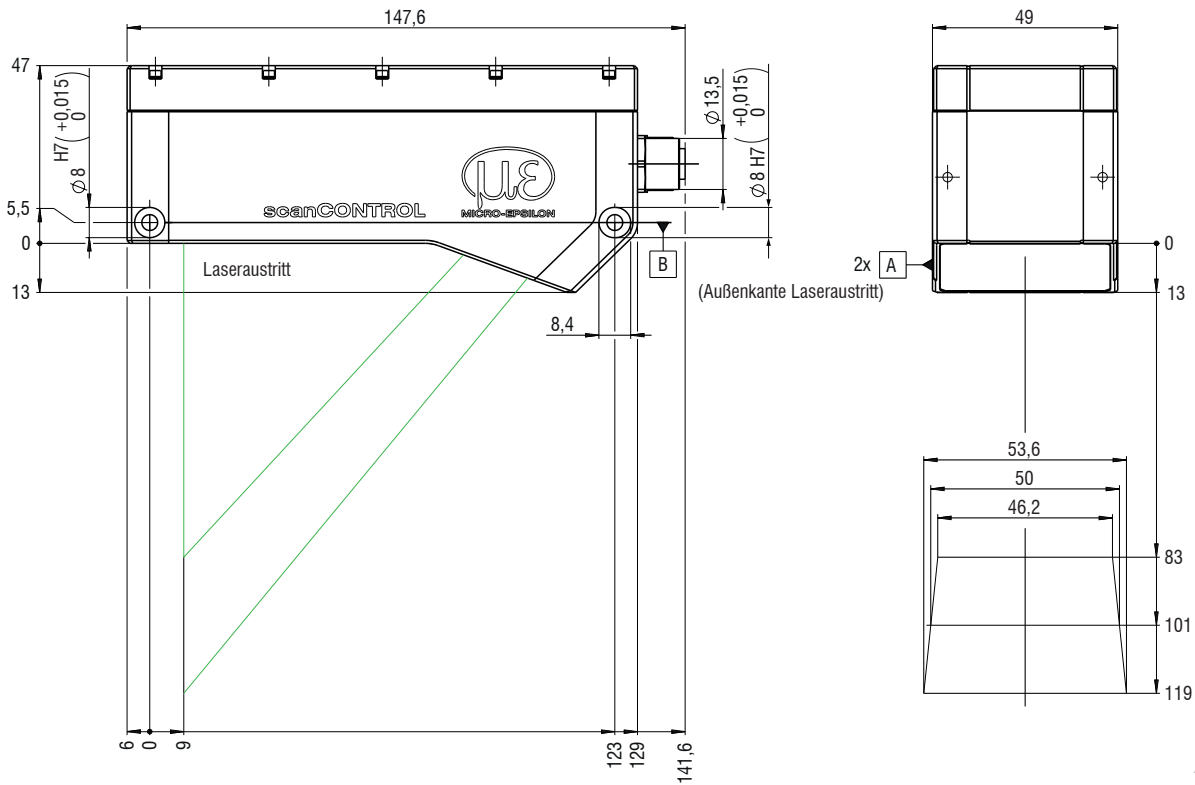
Maßzeichnung Montagebohrung Draufsicht
